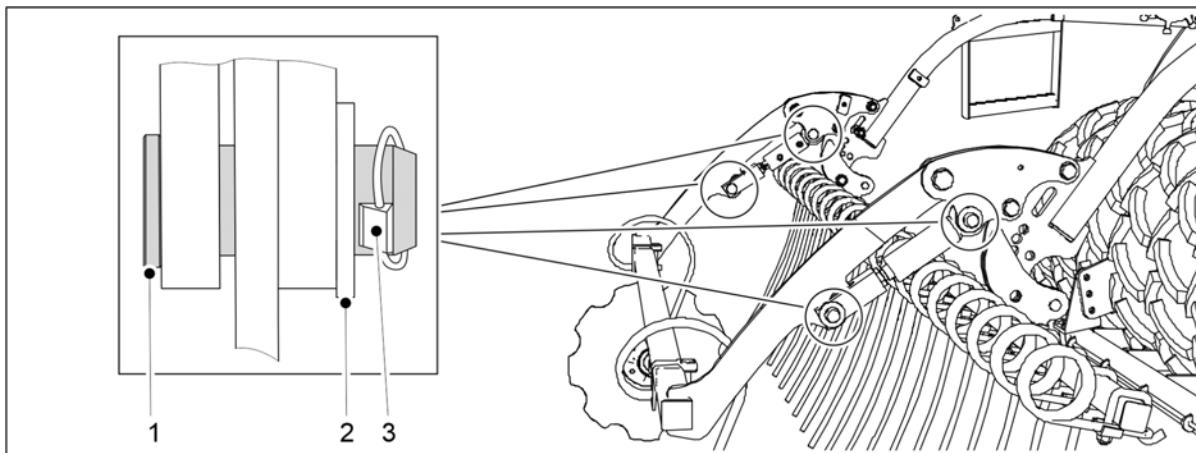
87. Montáž zadních značkovačů na zadní brány
